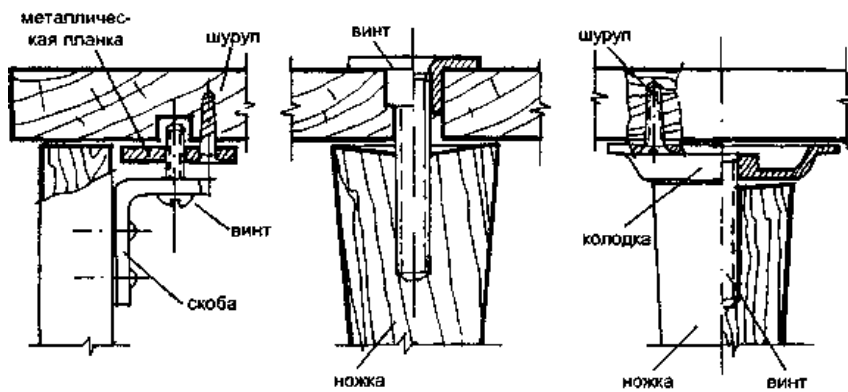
2. Схемы соединений мебельными резьбовыми стяжками.
